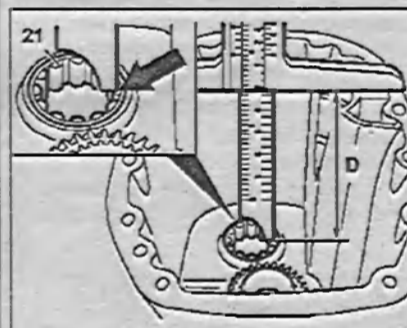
Измерьте размер «D» от передней части корпуса коробки передач до цилиндрического ролика (стрелка) подшипника 21.
